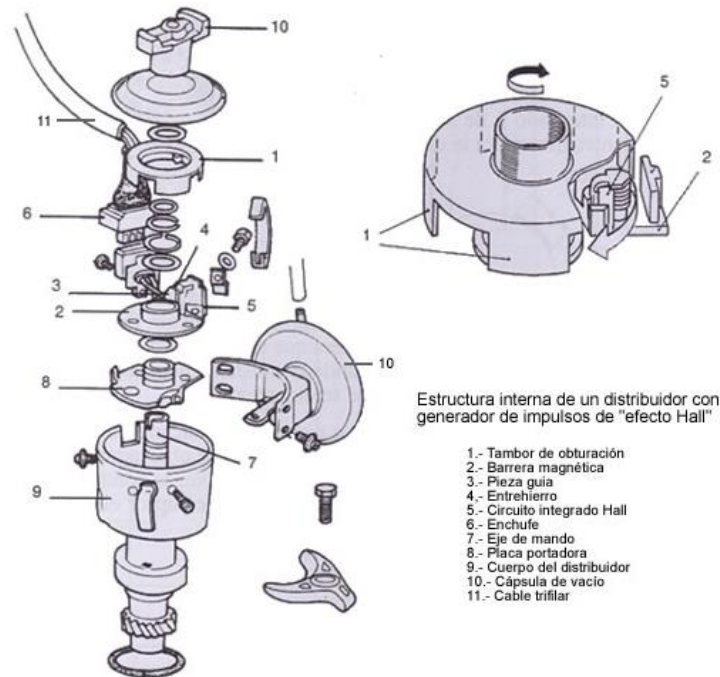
Despiece de un conjunto distribuidor [14].
